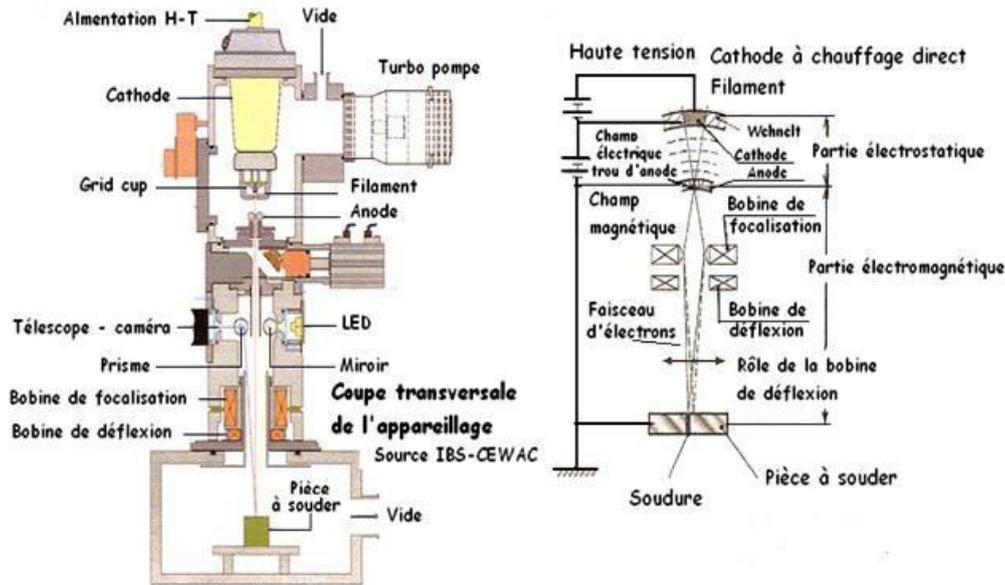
Principe du soudage par faisceau d'électrons.
